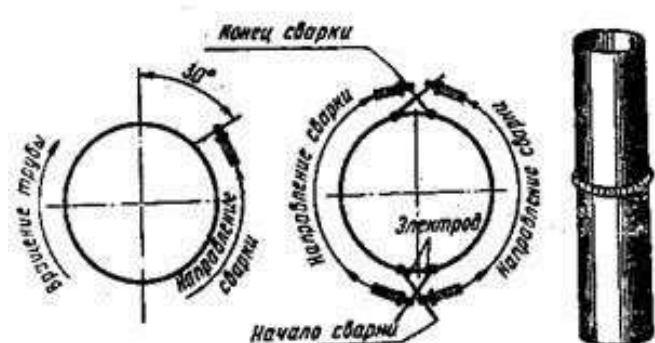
Сварные стыки труб: поворотный, неповоротный, горизонтальный
